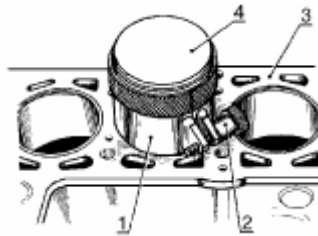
Схема встановлення поршня в циліндр.
